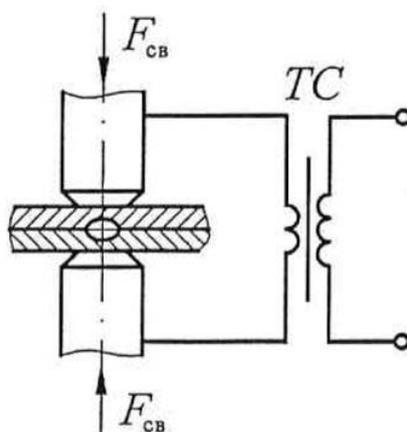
Упрощенная схема процесса контактной точечной сварки
